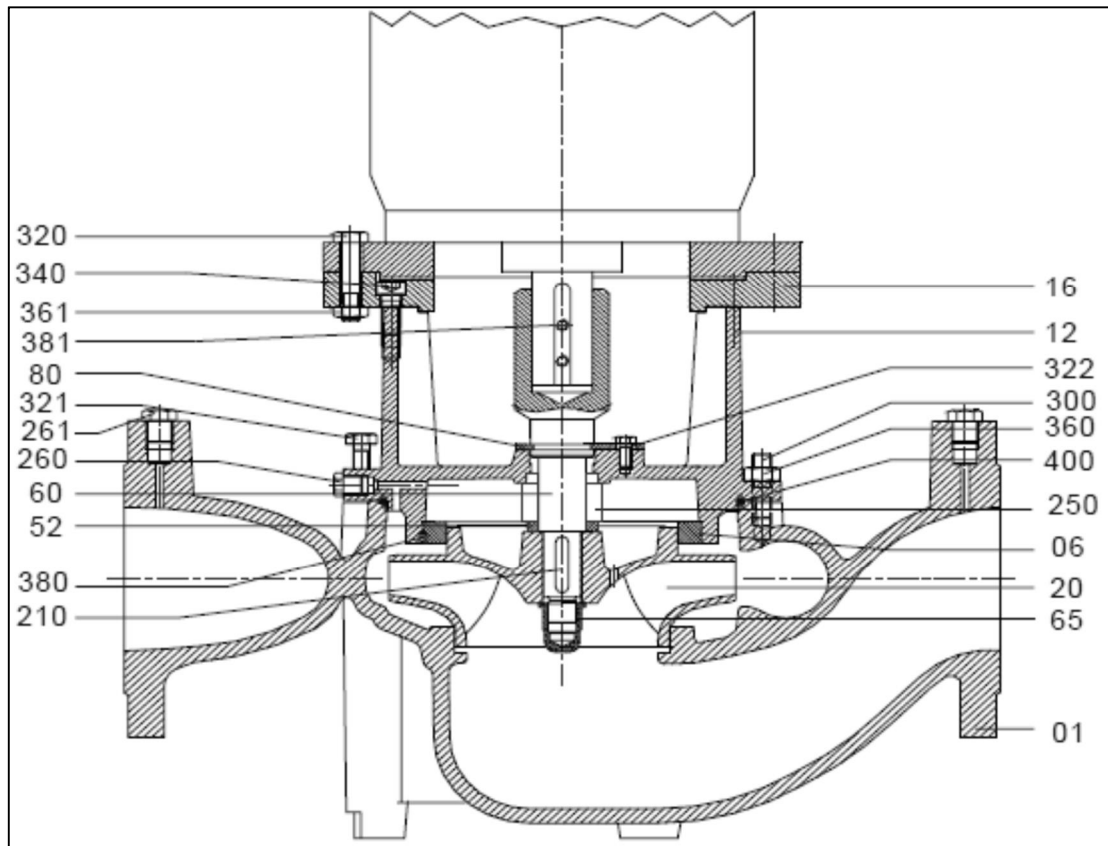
Schnittzeichnung SKI unter 30 kW
